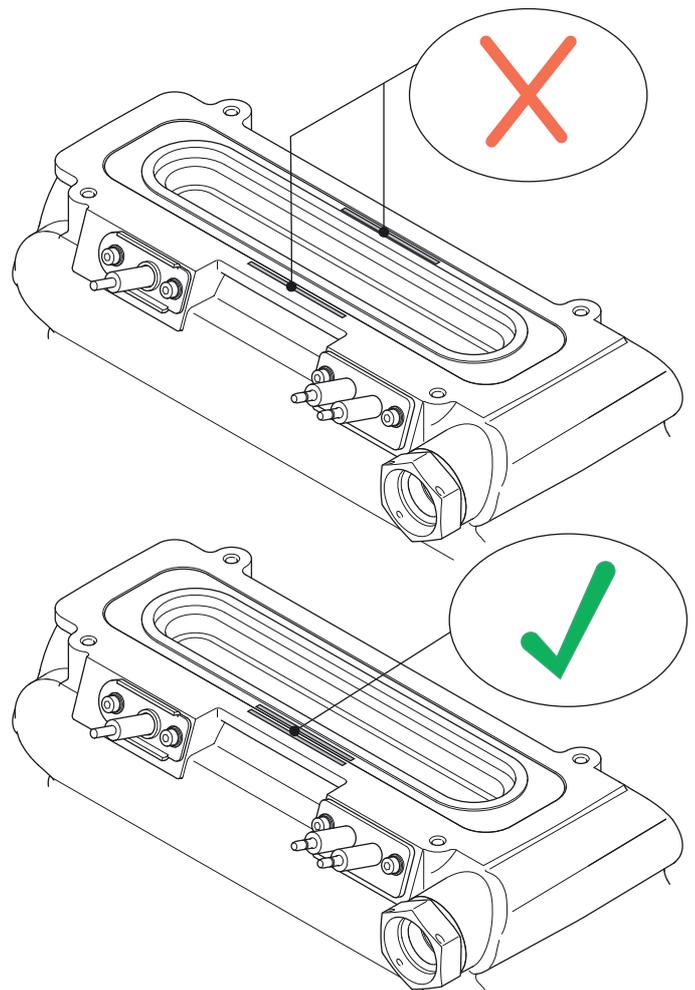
Brennereinbau - Sitz Brenneroberfläche auf Kesselkörper
